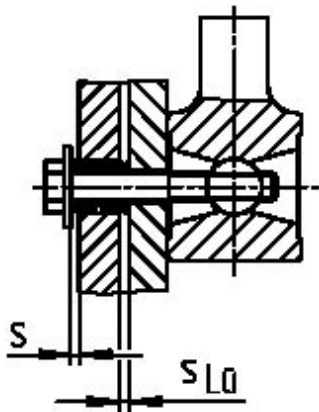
Änderung des Bremsmomentes / Adjusting the braking torque / Modification du couple de freinage
